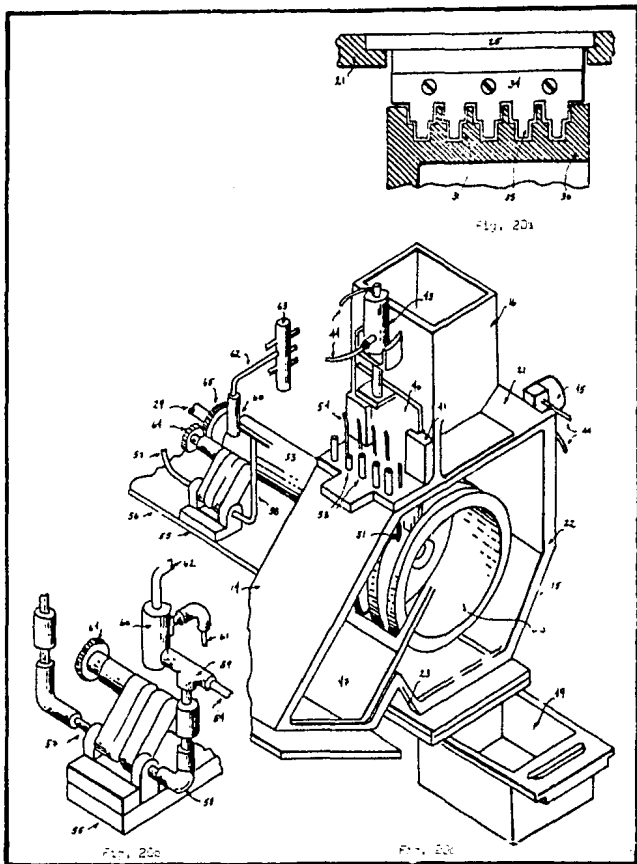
Figura isométrica de la rueda de platos ensamblada de acuerdo a la técnica de plateado. (64)
